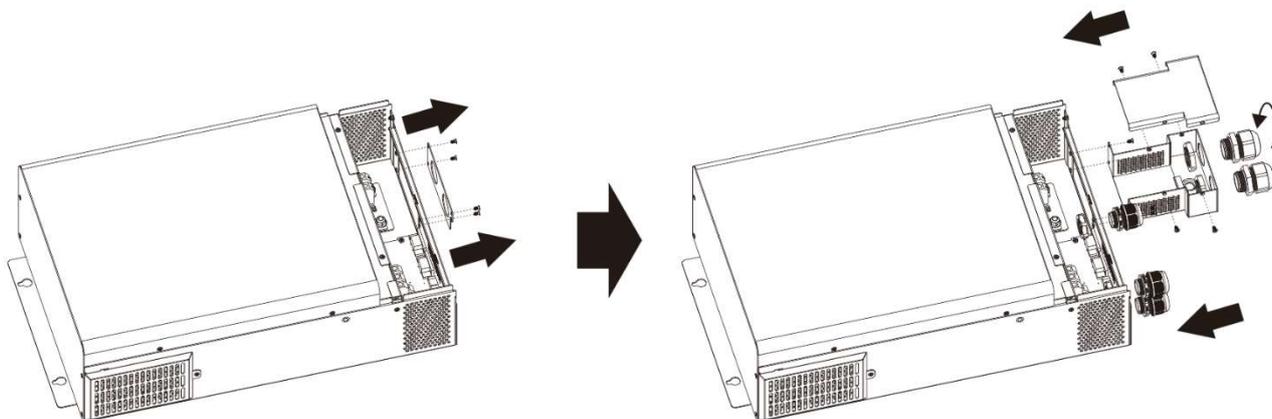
Installation des presse-étoupes et d'une boîte d'extension de câblage de batterie
